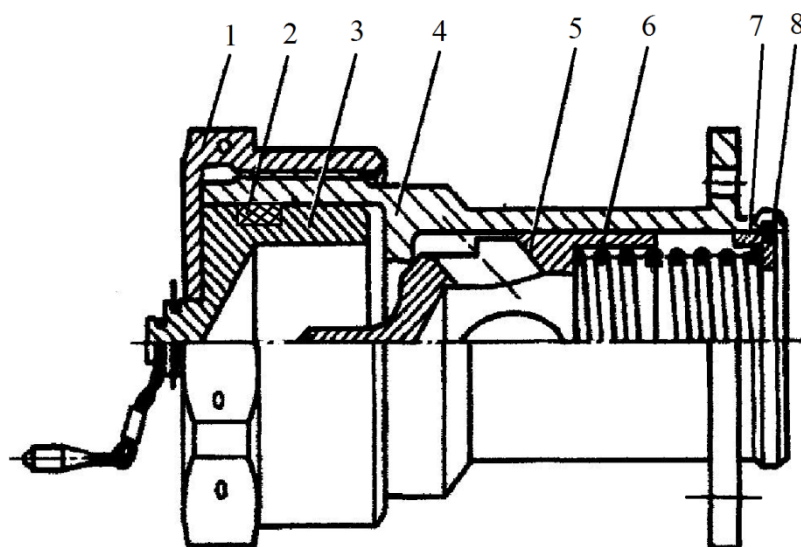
Бортовой клапан всасывания, где 1- крышка; 2- уплотнительный пакет; 3- заглушка; 4- корпус; 5- клапан; 6- пружина; 7- упорная втулка; 8- стопорное кольцо
